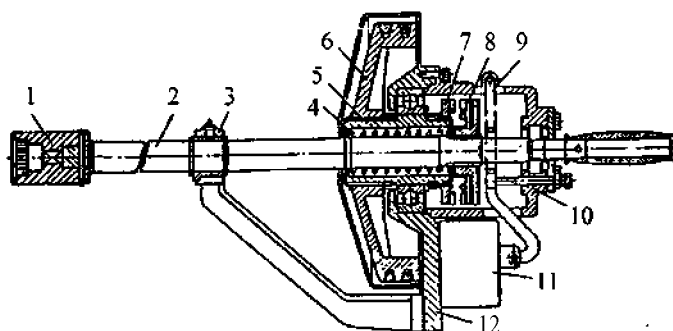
Ударный механизм гайковертов И 318 и И 330
